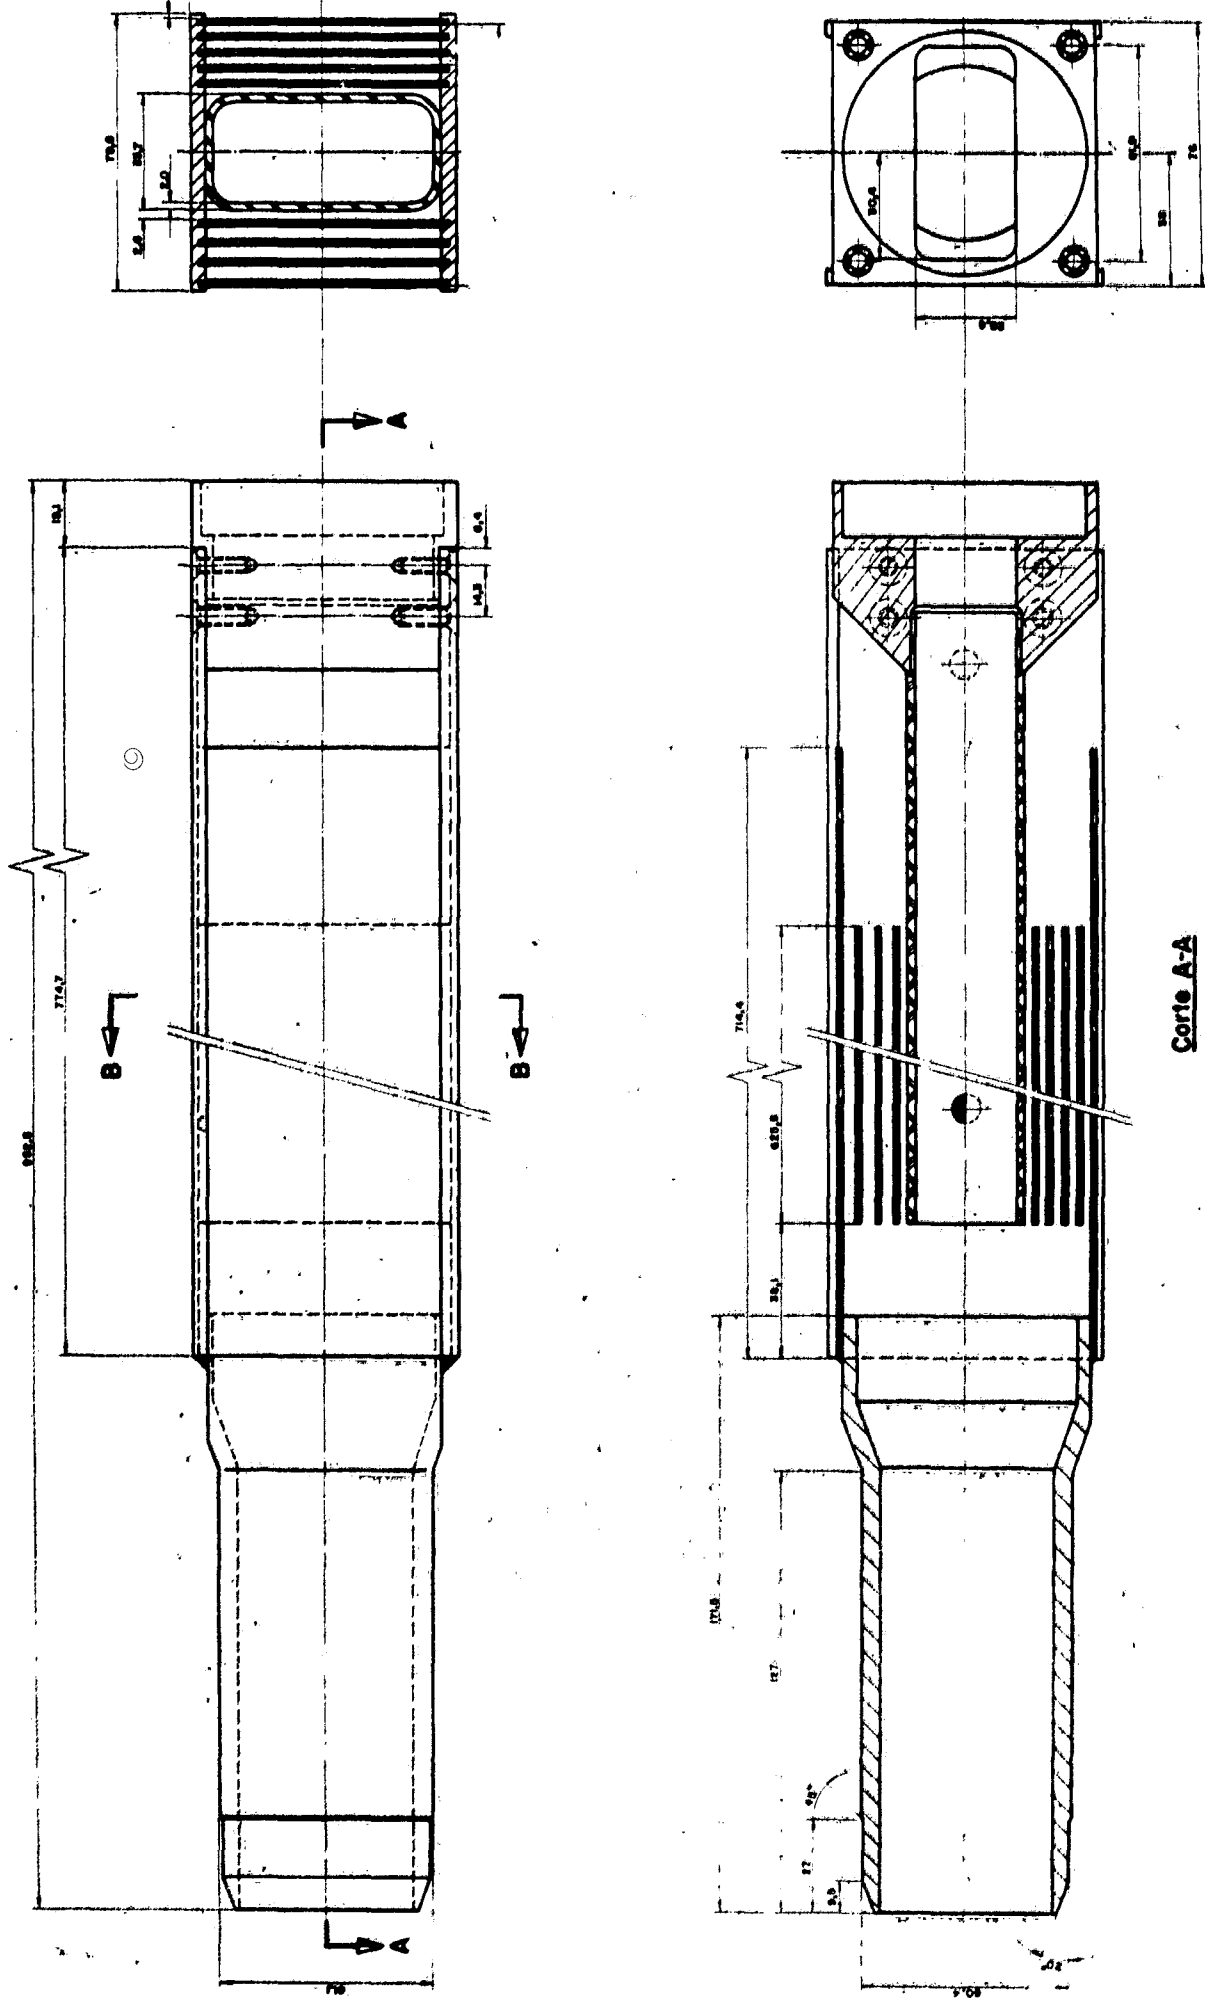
Elemento Combustível (dimensões em mm)
